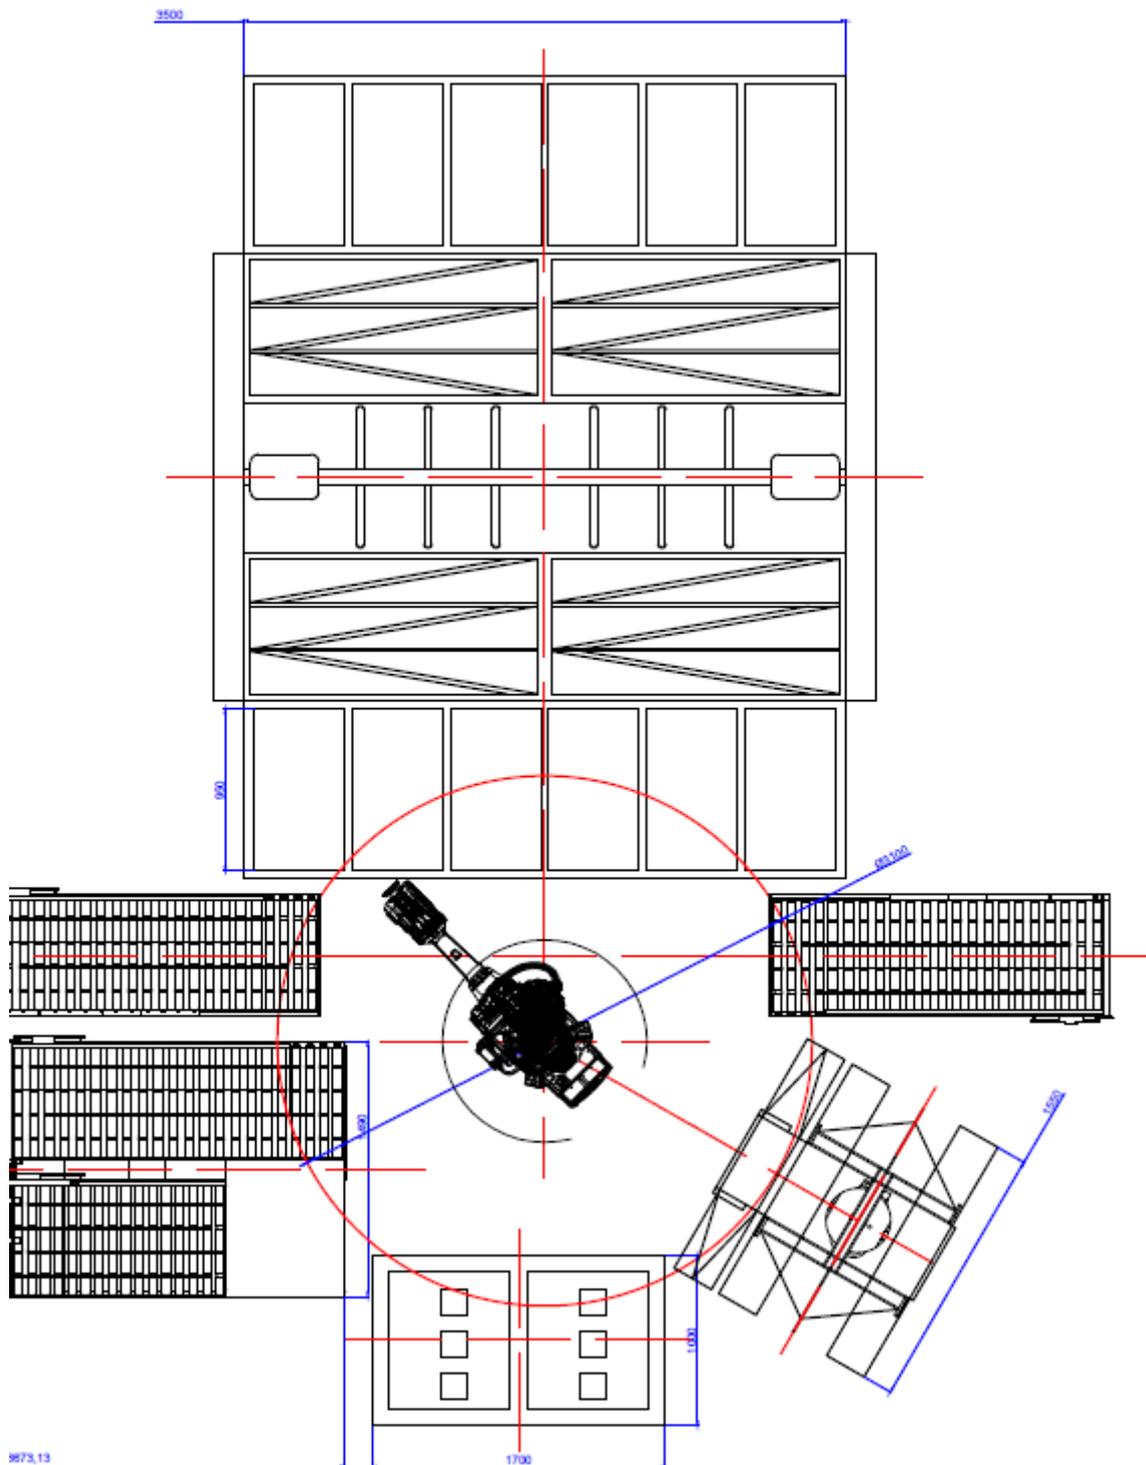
Planimetria proposta C.1: un solo robot al centro con trasferimento della zona d'assemblaggio
